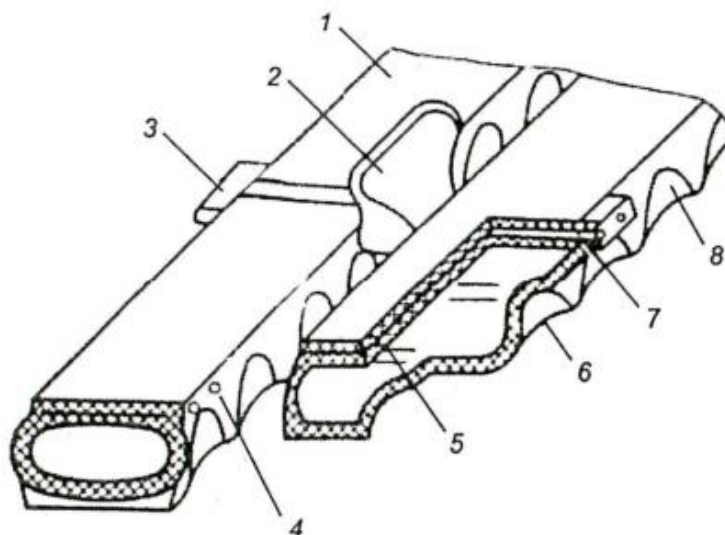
Схема устройства пневматической гусеницы: 1 - пневмотраки; 2 - гребни; 3 - цевки; 4, 8 - боковые поверхности; 5 - силовой пояс; 6 - опорная поверхность; 7 - соединительные пальцы.
